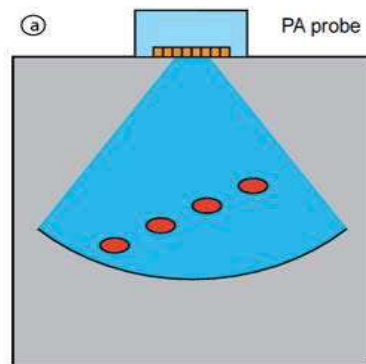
Inspección Ultrasónica para Dimensionar Discontinuidades
